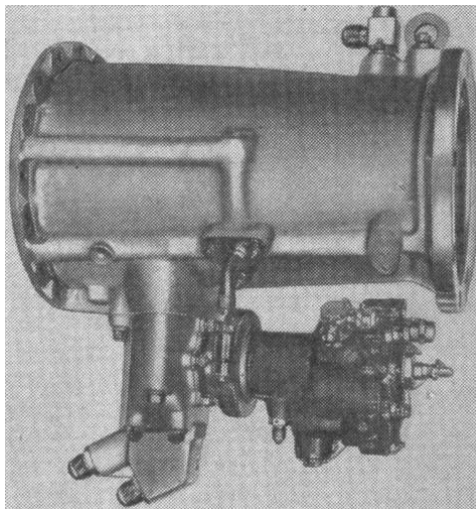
Корпус главного привода с установленным на нем агрегатом РО-40ВР
